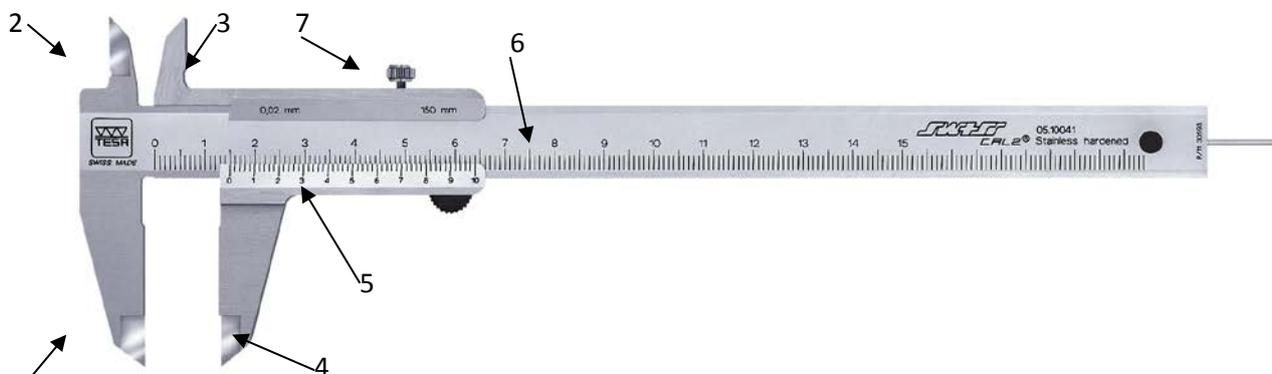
Устройство штангенциркуля. 1,2 – неподвижная губка, 3,4 – подвижная рамка, 5 – нониус, 6 – шкала штанги, 7 – винт для зажима рамки
